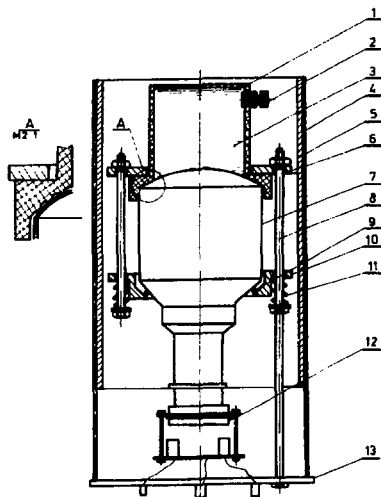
Конструкция нейтронного детектора: 1 - кювета из фторопласта-4; 2 - уплотняемый патрубков; 3 - жидкий сцинтиллятор; 4 - корпус; 5 - магнитный экран; 6,10 - фланцы; 7 - ФЭУ типа 58AVP; 8 - шпилька; 9 - прокладка; 11 - пружина; 12 - панель с делителем напряжения; 13 - задняя крышка с разъемами.
